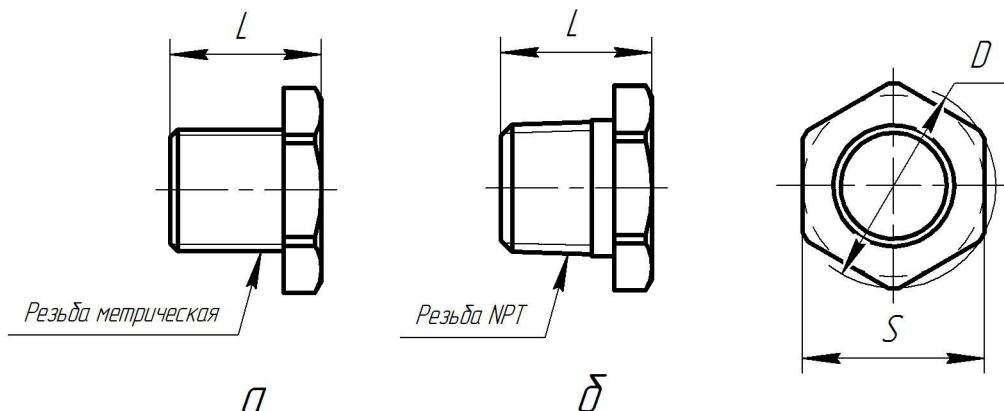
а - заглушки с метрической резьбой, б - заглушки с NPT резьбой
